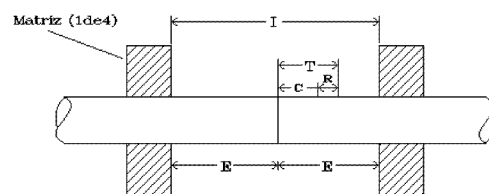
Dimensões Características para a Soldagem por Centelhamento
